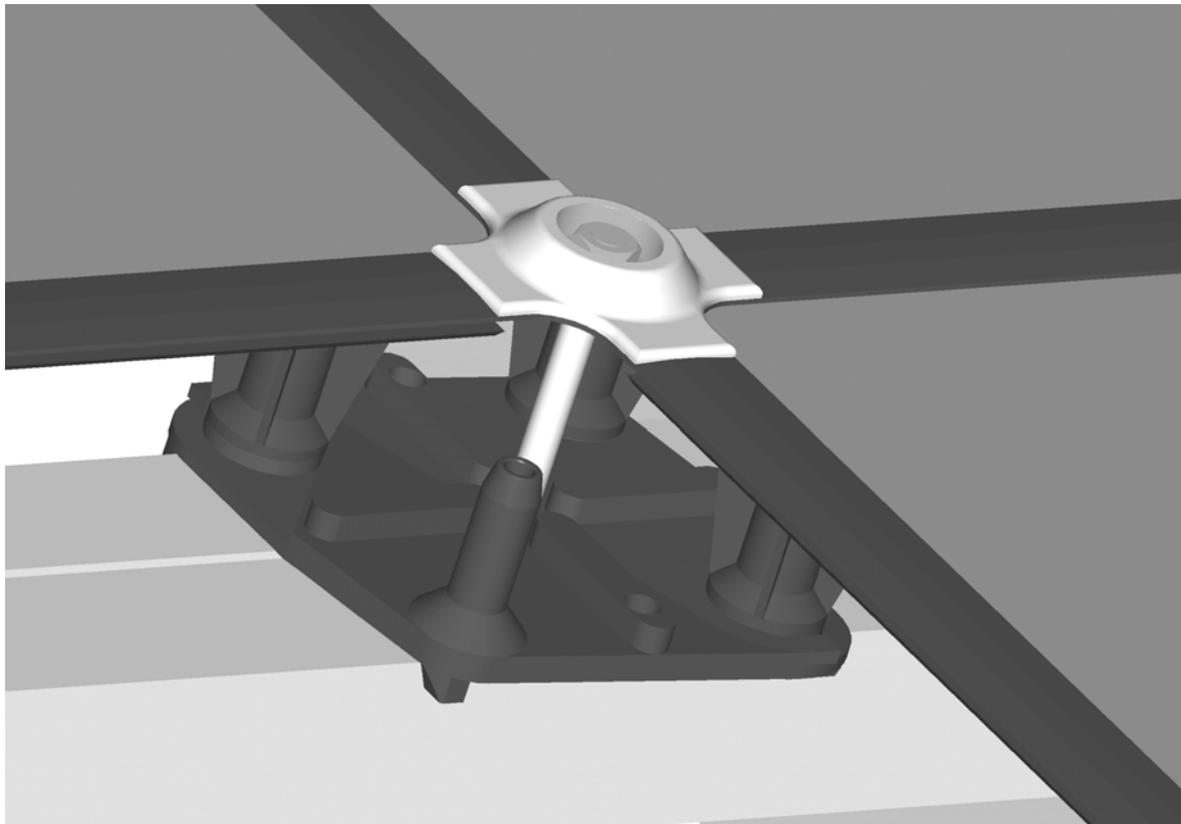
Eingebaute Baugruppe zur Fixierung der PV-Module auf den Trägerprofilschienen, Indach-Variante
